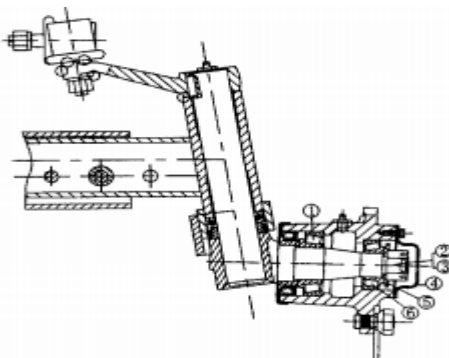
Регулировка осевого зазора подшипника переднего колеса
